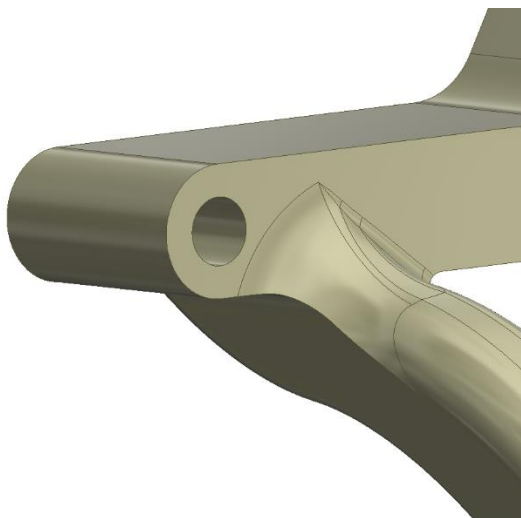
Přední nápravová tyč - díra pro spojení s přední spojovací součástí
